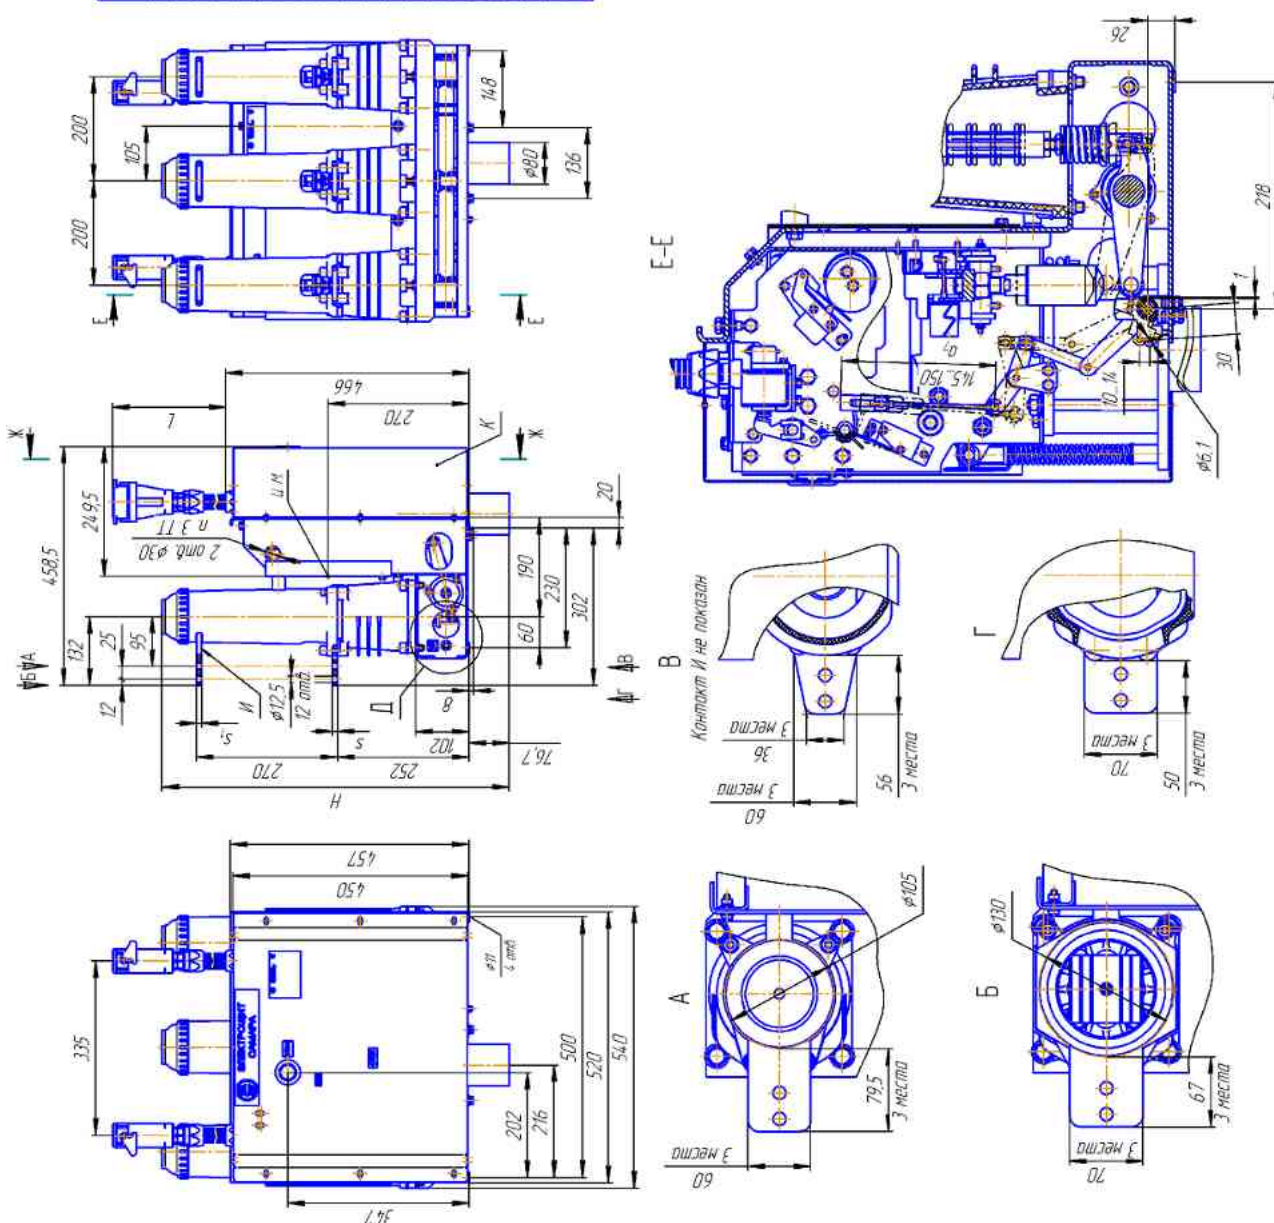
Габаритные, установочные и присоединительные размеры выключателя типа ВВУ-СЭЦ-ЭЗ-10. Тип подключения – два жгута с разъемами
